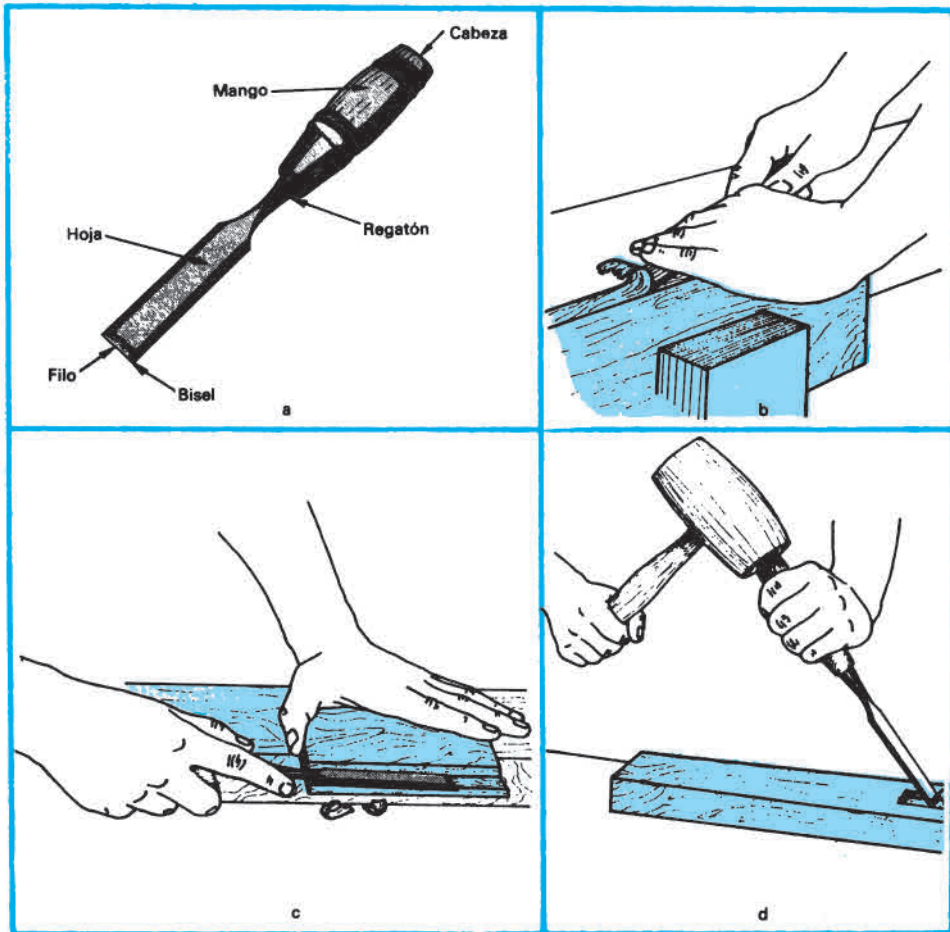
Formones o trinchas: a) partes; b, c y d) uso de los formones o trinchas.
